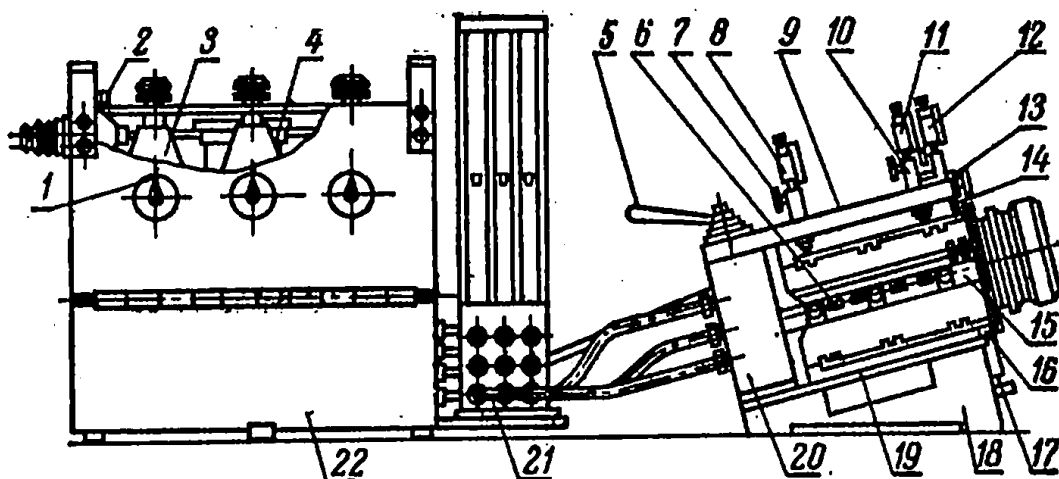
Устройство приспособления для контроля гильз цилиндров:
